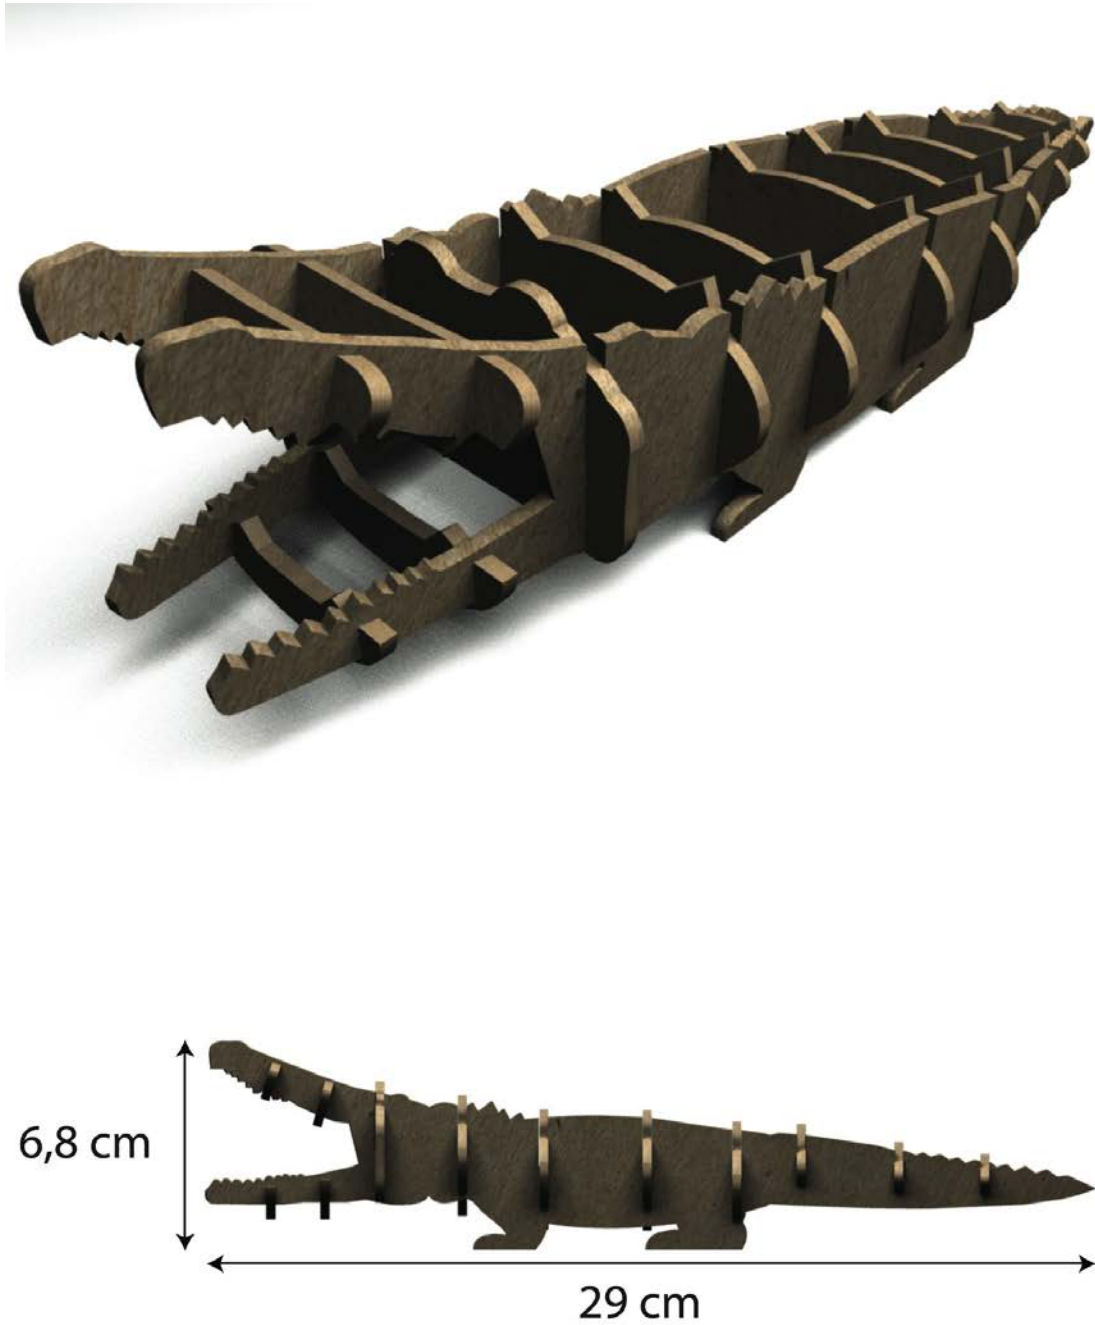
Vista 3D del cocodrilo armado y vista lateral.
